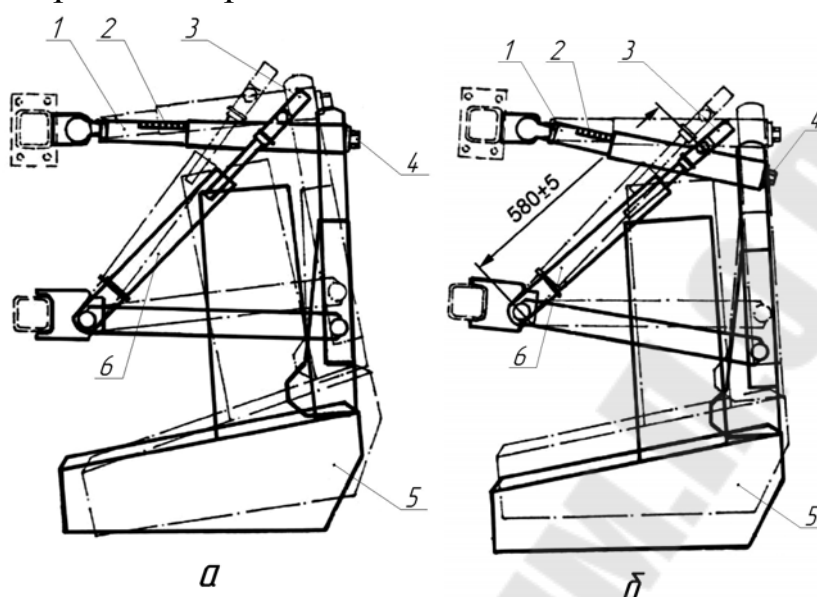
Схема механизма крепления валкоукладчика к раме: а – схема регулировки угла наклона; б – схема регулировки по высоте; 1, 6 – тяги; 2 – линейка; 3, 4 – винты регулировочные; 5 – валкоукладчик
